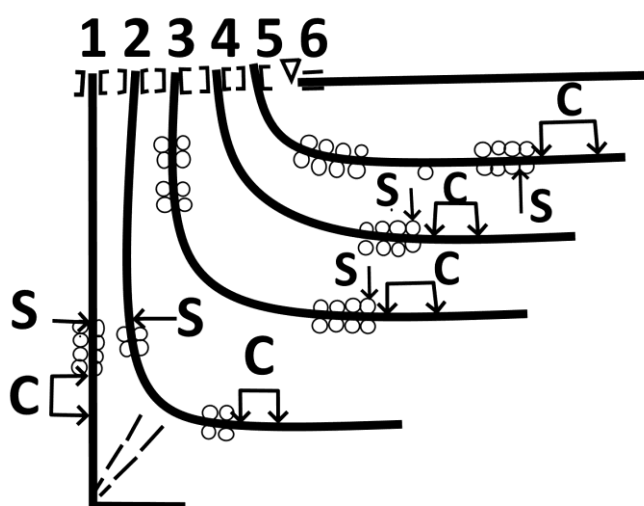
Принципові схеми машин безперервного лиття заготовок
